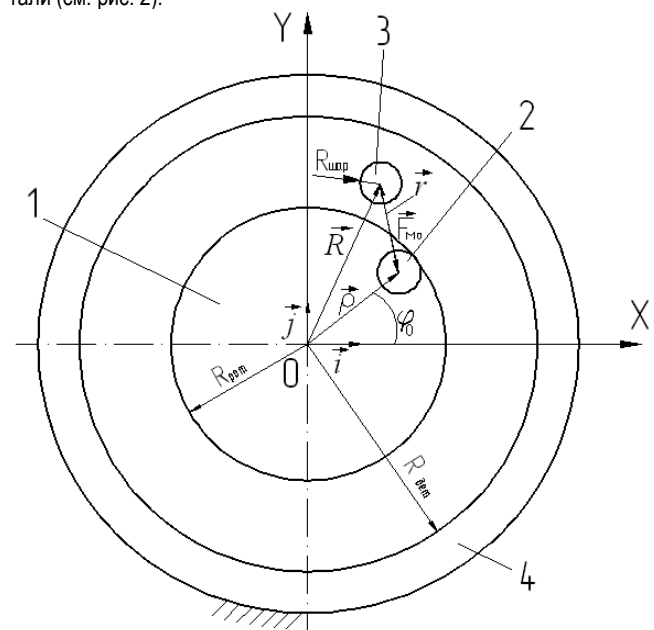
Схема движения деформирующего шара от поверхности магнитного ротора до упрочняемой детали (1 – ротор инструмента; 2 – источник магнитного поля; 3 – деформирующий шар; 4 – обрабатываемая деталь)
